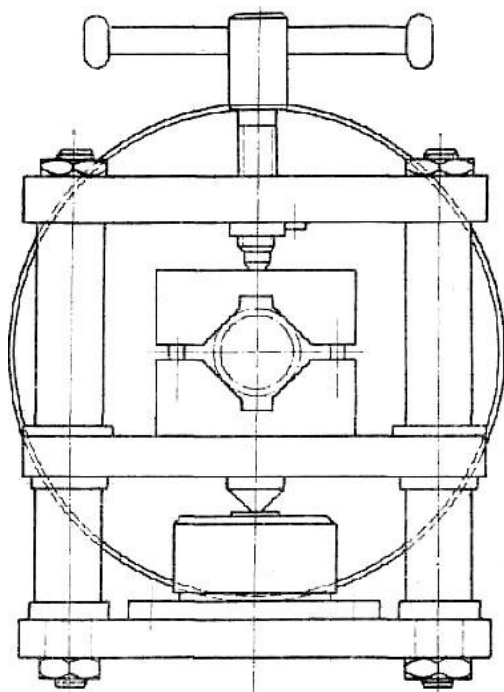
Приспособление с гидравлической месдозой для закрепления заготовок
